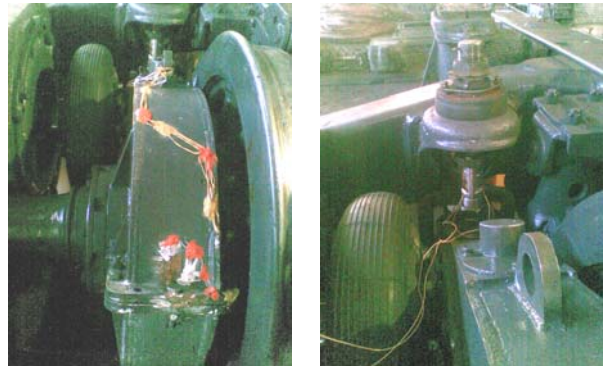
Тяговий редуктор з вимірювальними пристроями
